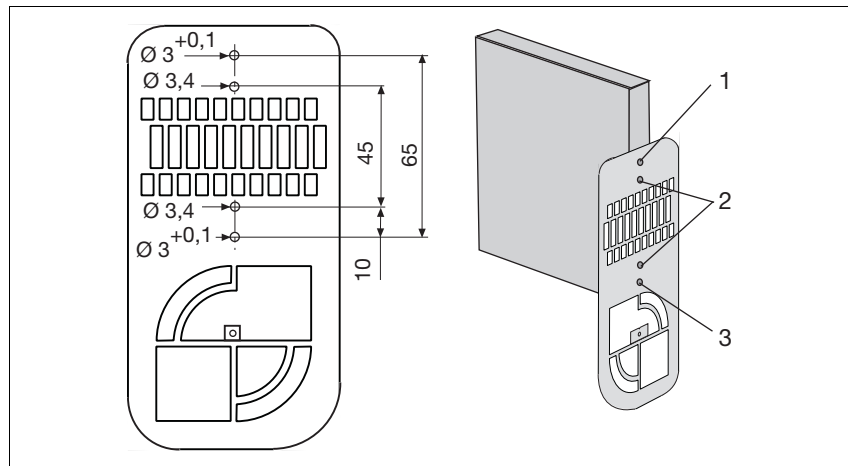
Justageschablone zum Anbringen an einen Träger
